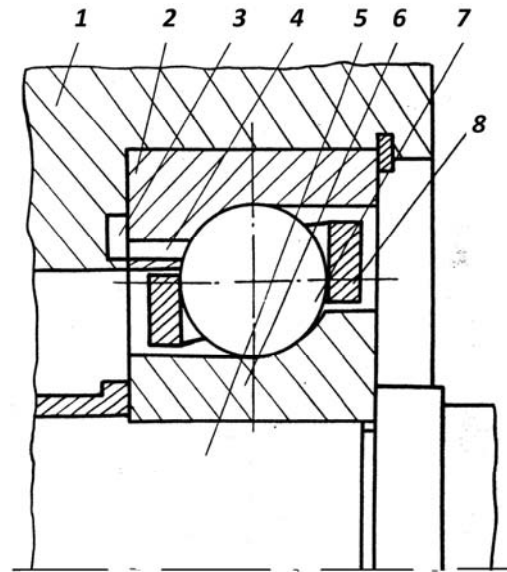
Передаточний механізм, що перетворює пневматичний тиск в осьові коливання шпинделя
